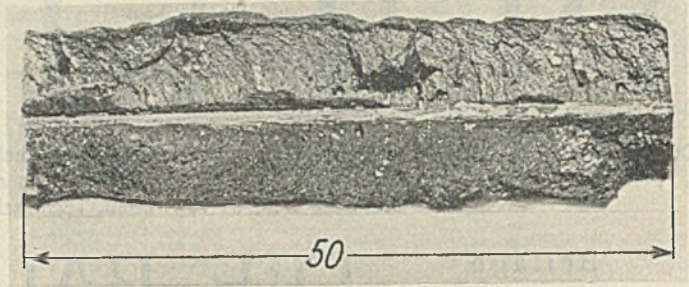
Bruchfläche einer X-Naht mit offener Fuge. Lichtbogenschweißung (Seelenelektroden) nach oftmals wiederholter Zugbelastung.
